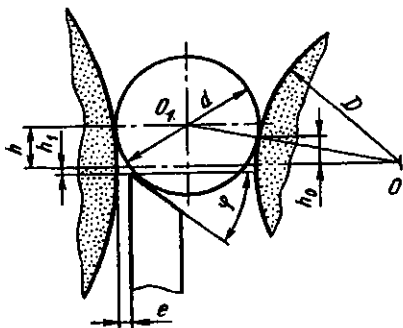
Схема регулирования опорного ножа и установки детали на бесцентрово-шлифовальном станке
